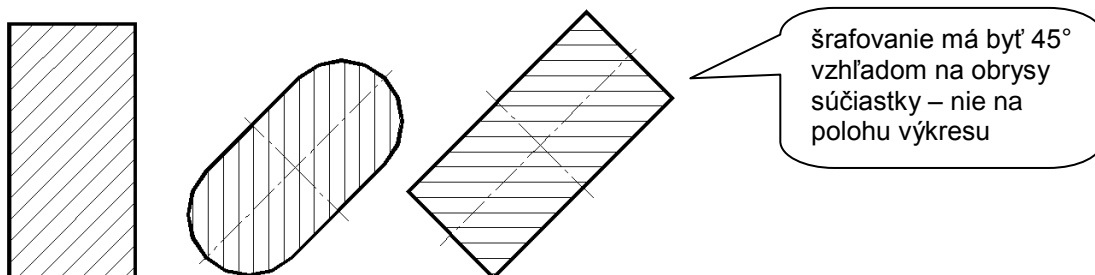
Zobrazenie rezov pomocou pootočených prierezov
